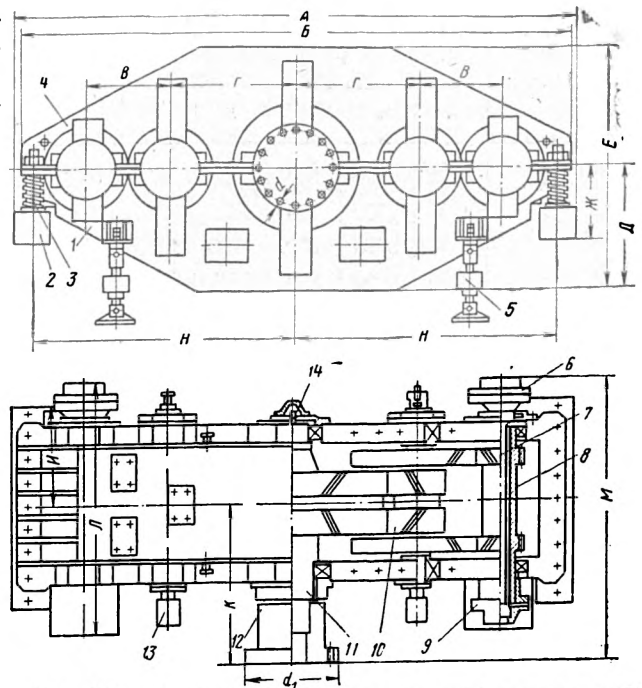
Двухприводный подпружиненный редуктор 2ЦД
